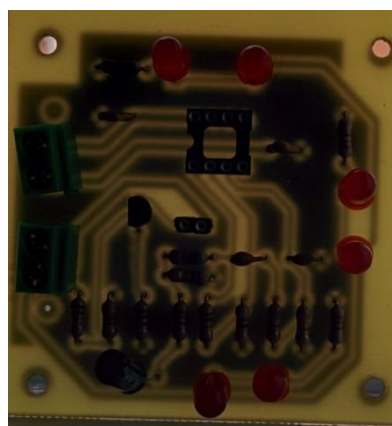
Placa del circuito impreso del emisor con los componentes soldados
